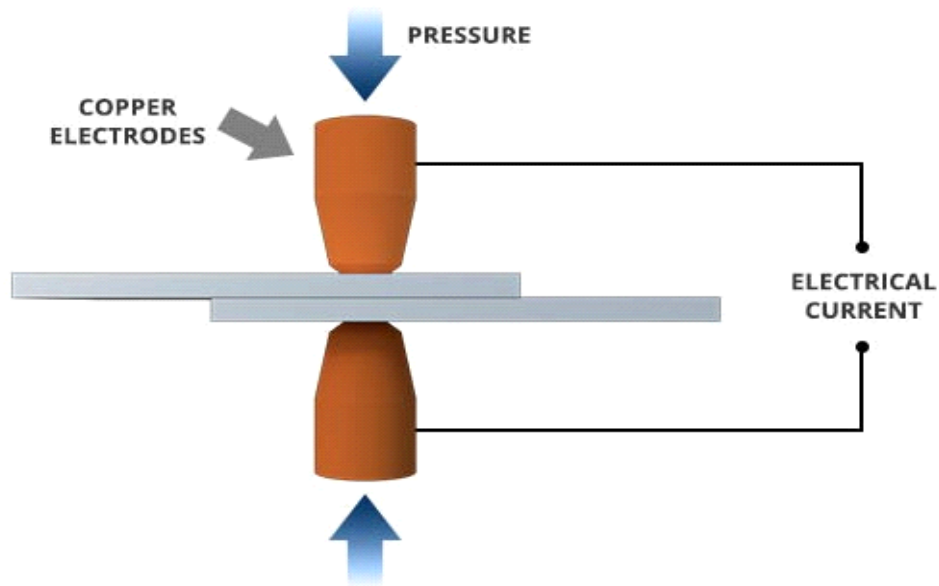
Schéma de principe du soudage par points par résistance.
